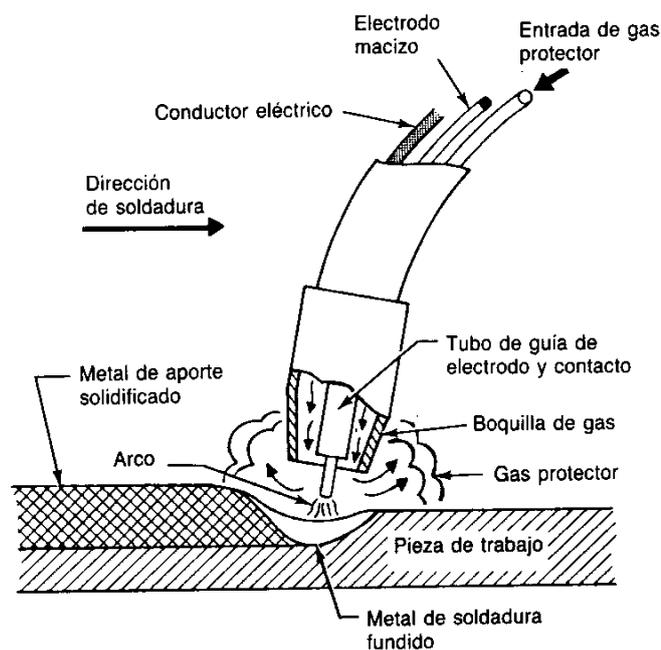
Variables que intervienen en el proceso de soldadura MIG /MAG
